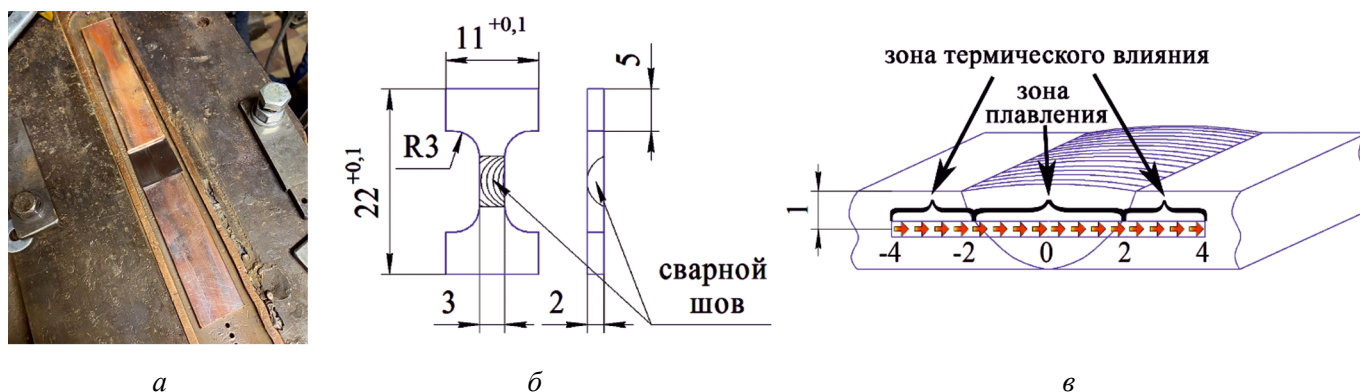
Внешний вид приспособления для аргодуговой сварки (а), образцы для проведения механических испытаний (б) и исследования микротвердости (в) сварных соединений из сплава ВТИ-4
